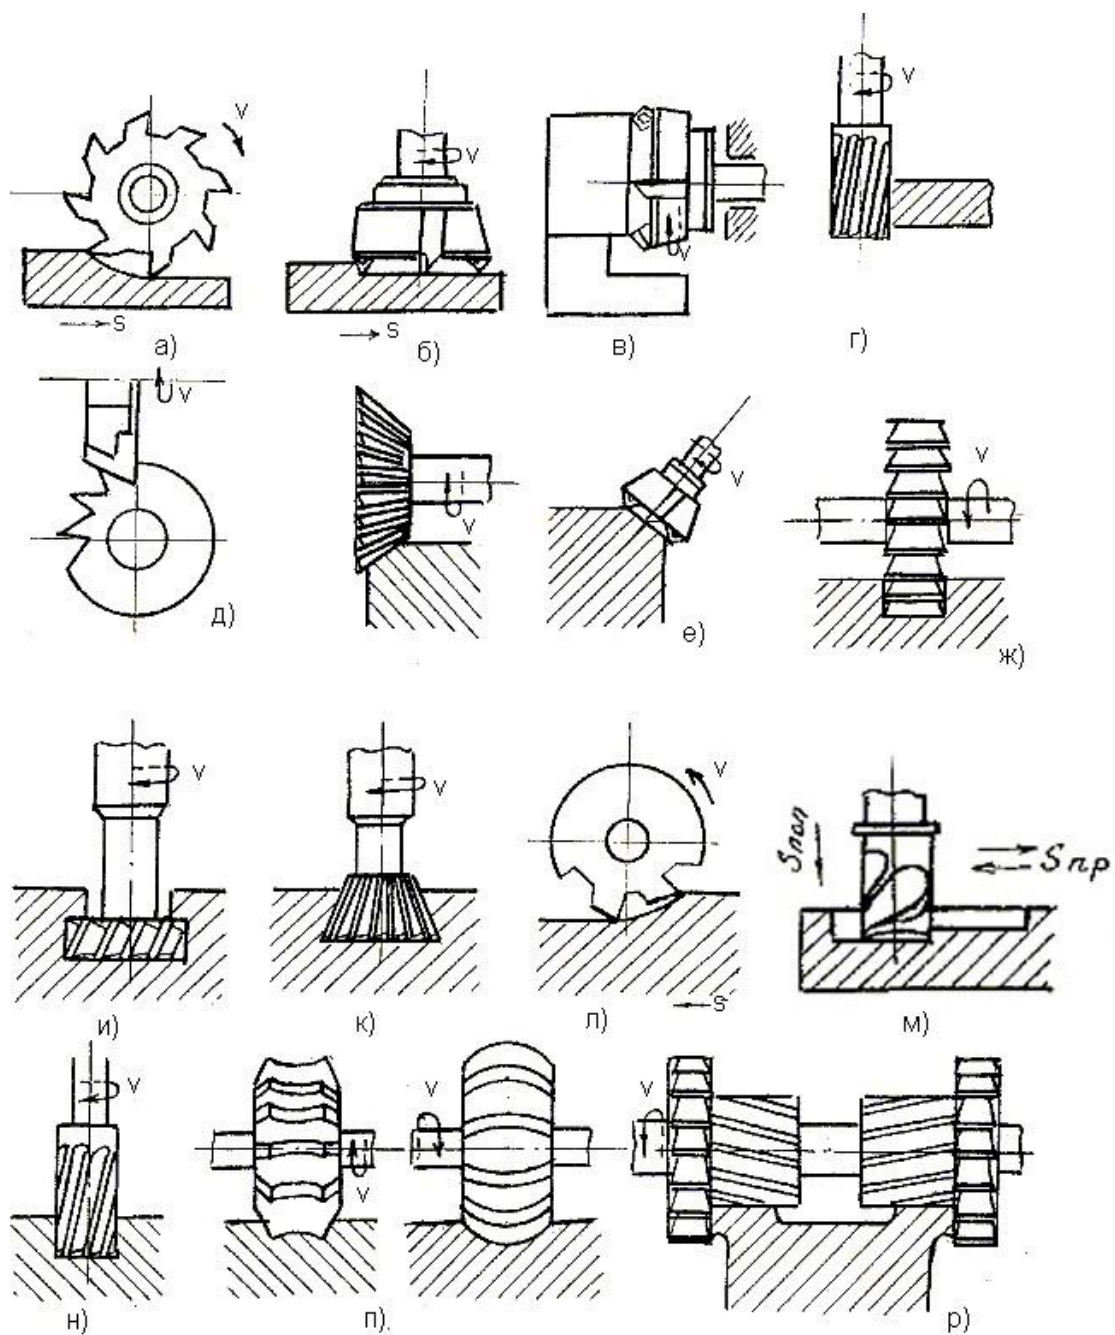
Приклади робіт, що виконуються на фрезерних верстатах
